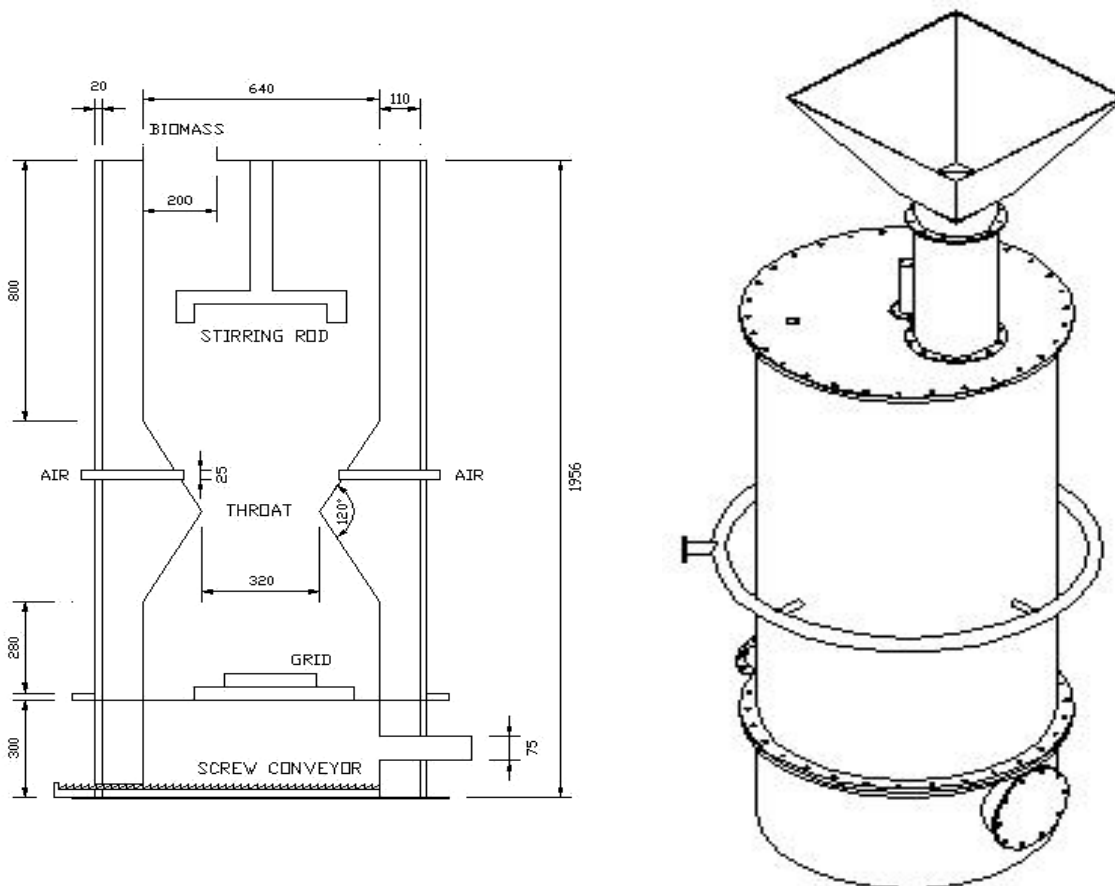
Principales dimensiones (mm) e isométrico del gasificador
